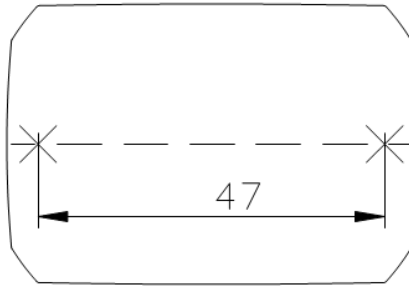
Габаритные и установочные размеры корпуса «С2000-WiFi»
